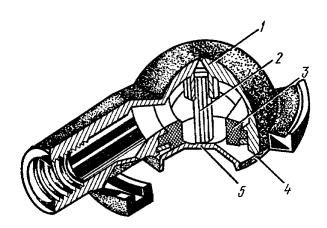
Головка соединительная типа «Б»: 1 — корпус; 2 — стержень; 3 — кольцо уплотнительное; 4 — гайка прижимная; 5 — крышка
